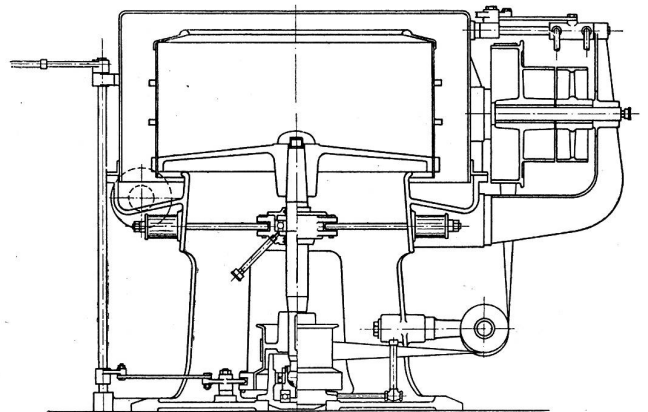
a) Zentrifuge mit festem Ständer und auf Gummipuffer elastisch gelagerter Welle.
